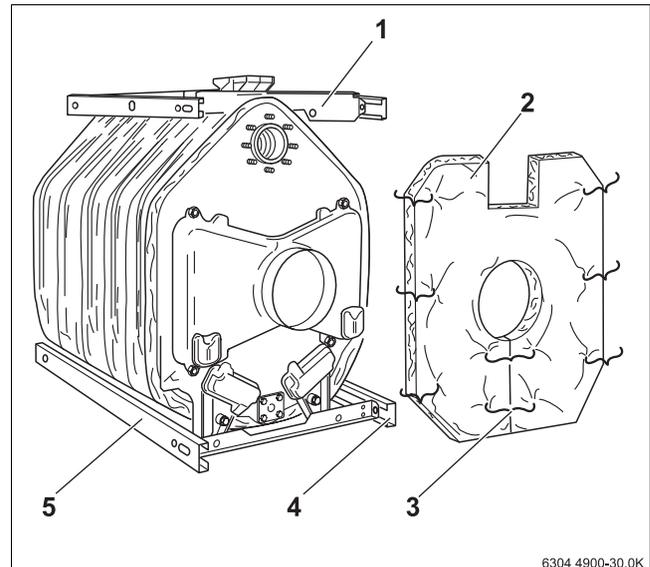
Untere Längstraversen und Wärmeschutz montieren
